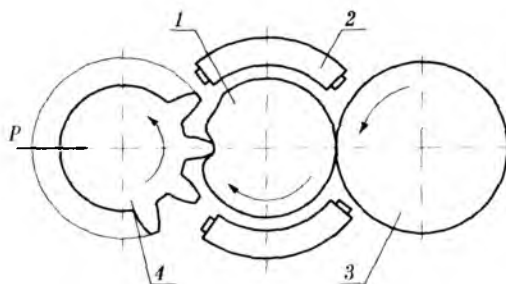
Схема горячей накатки зубьев шестерни:
